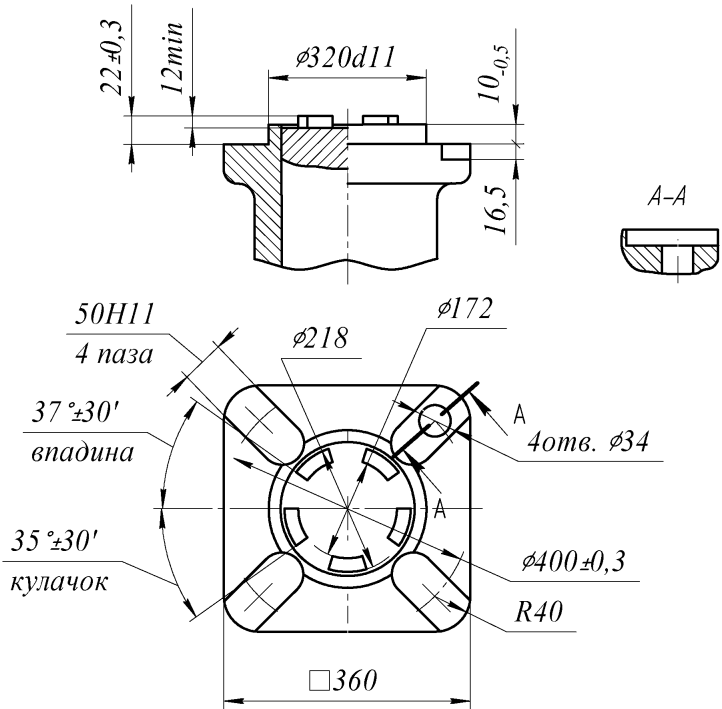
Ответное присоединение трубопроводной арматуры типа Д
